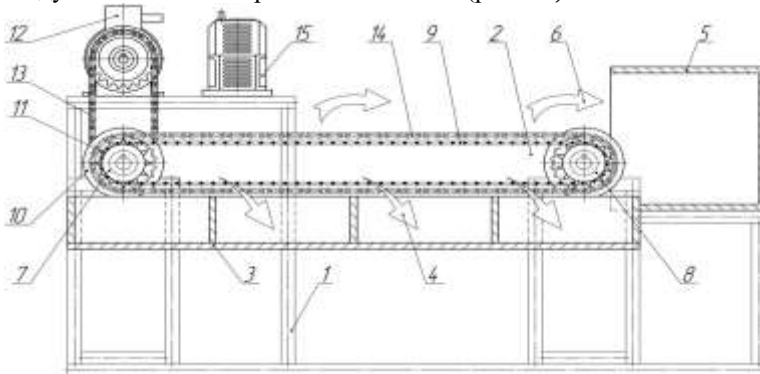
Схема экспериментальной установки: 1 – рама; 2 – транспортер; 3 – емкость для сбора свободного зерна; 4 – свободное зерно; 5 – емкость для сбора вороха; 6 – ворох, идущий сходом; 7 и 8 – барабан; 9 – сетчатое полотно; 10 – реборда; 11 – выступы на поверхности барабанов; 12 – электродвигатель; 13 и 14 – цепная передача; 15 – частотный преобразователь
